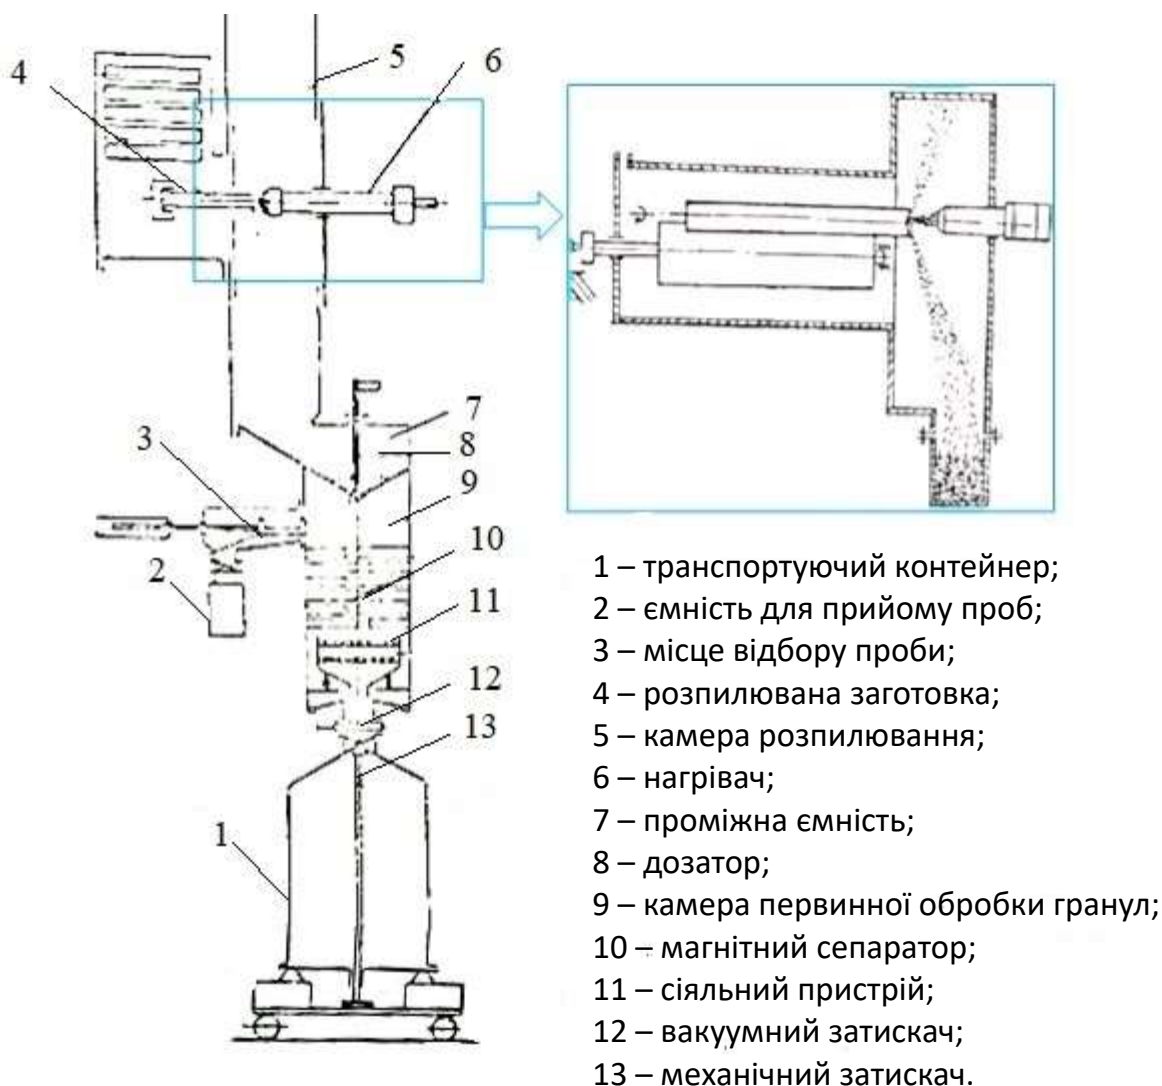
Схема установки для ротаційного плазмового розпилення
